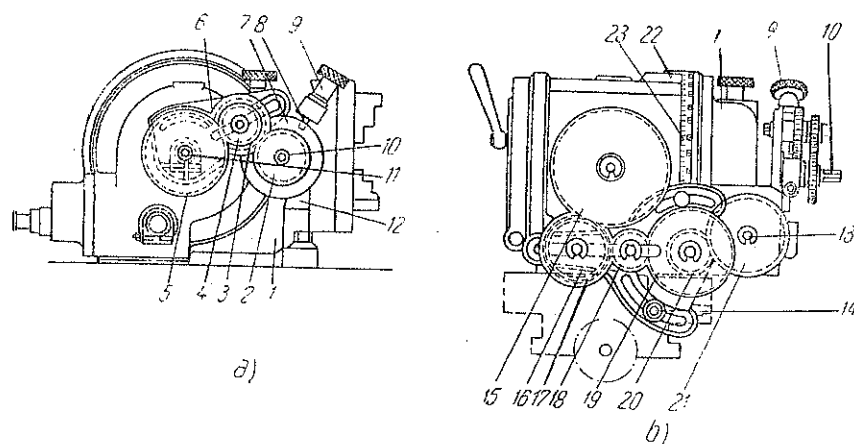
Cap divizor universal cu mecanism planetar (v. și fig. 7.104):
